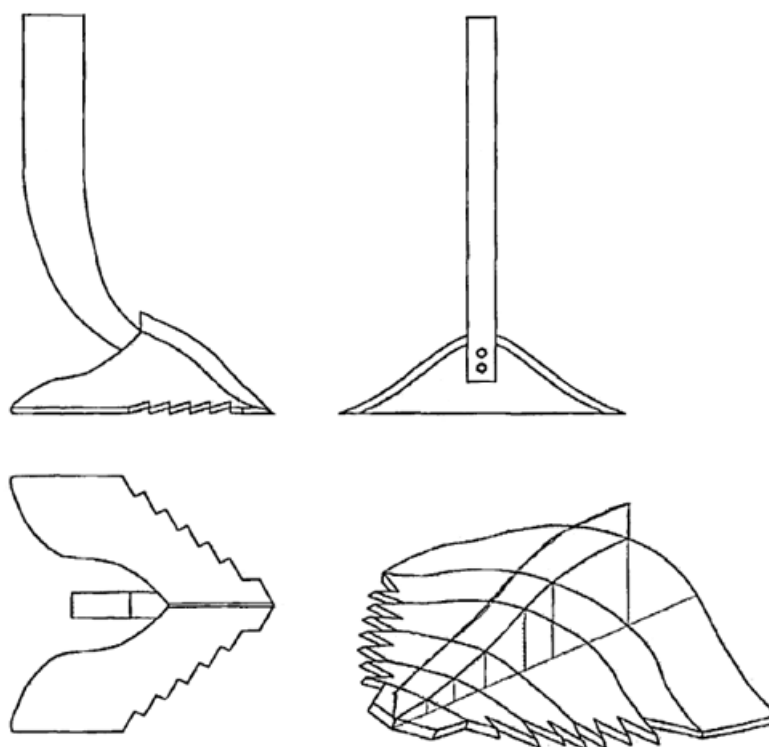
Робочий орган культиватора для передпосівної обробки ґрунту
